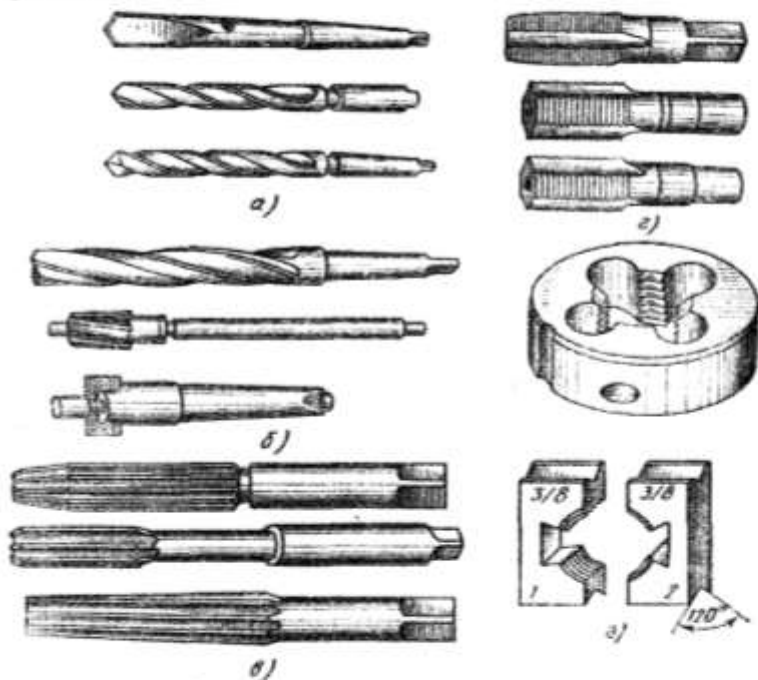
Набор металлорежущего инструмента: а — сверла, б — зенкеры, в — развертки, г — метчики, д — плашки
